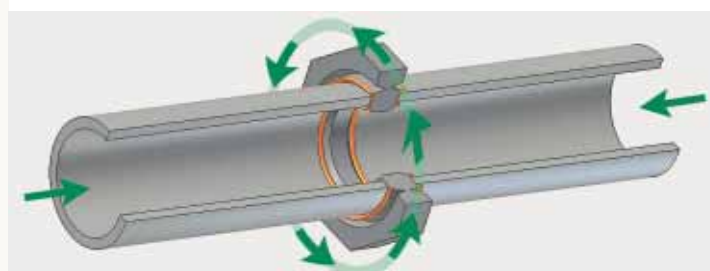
Principe de la nouvelle variante du procédé de soudage par friction
